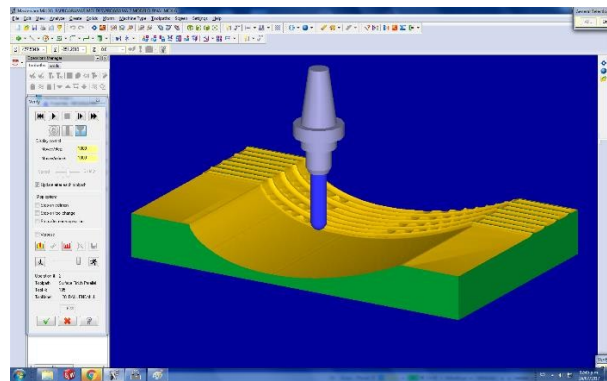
Segmento Molde según Dimensiones de Bancada. (Fuente: Autor).
